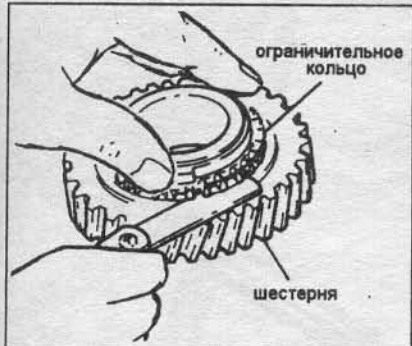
Проверка зазора в паре синхронизатор/шестерня.
